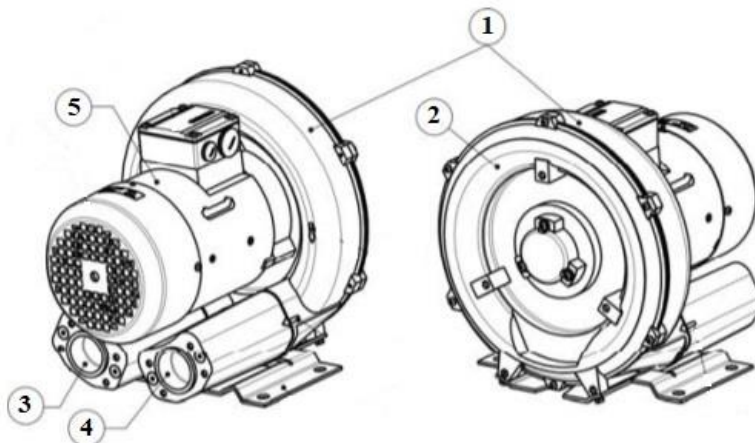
Radiální ventilátor [14]: 1-Oběžné kolo, 2-Sací hrdlo, 3-Výtlačné hrdlo, 4-Spirální skříň, 5-Elektromotor
